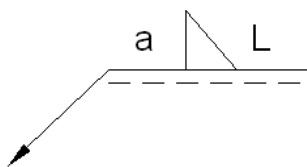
Cordón de soldadura por el lado de la flecha
